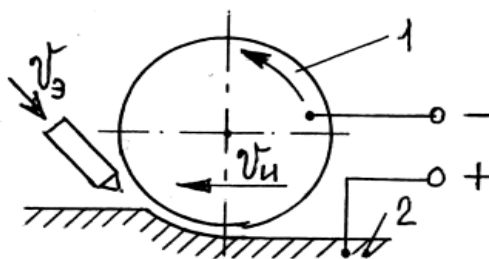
Схема шліфування: 1 – електрод-інструмент; 2 – заготовка
